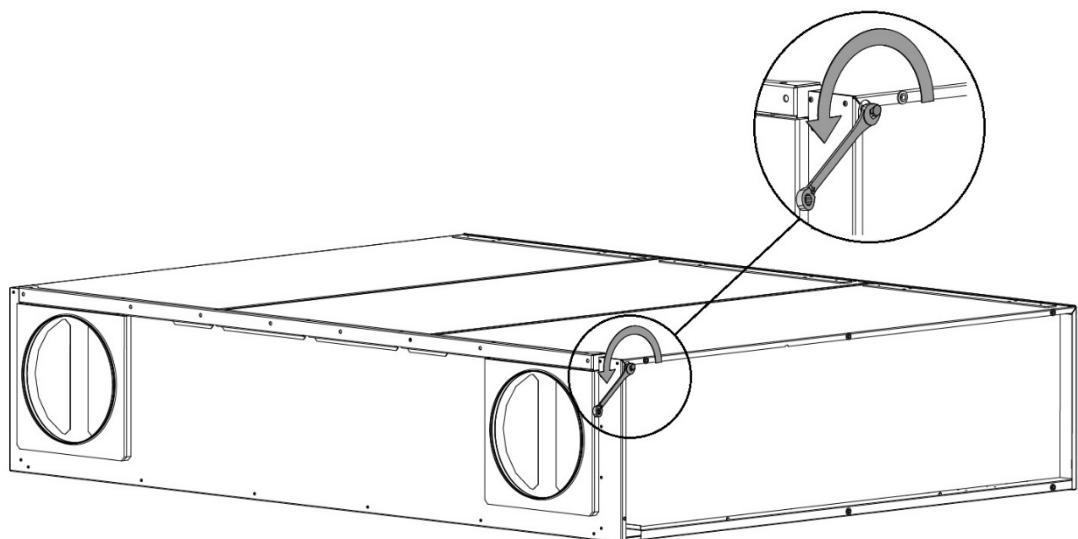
Démonter le support arrière, côté droit vu de derrière
